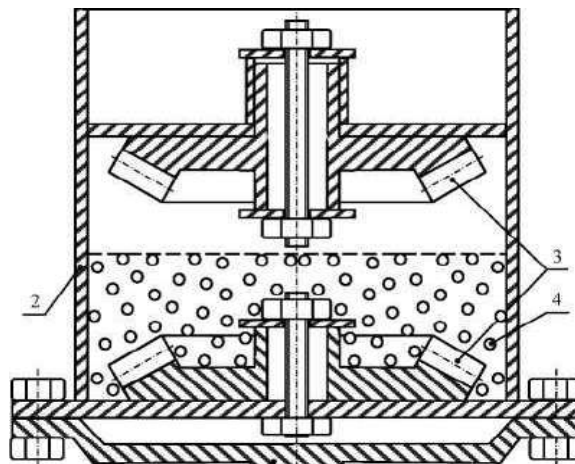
Встановлення конічних шестерень у робочій камері для динамічного наклепу поверхонь зубів сталевими кульками із введенням порошку фторованого графіту:
